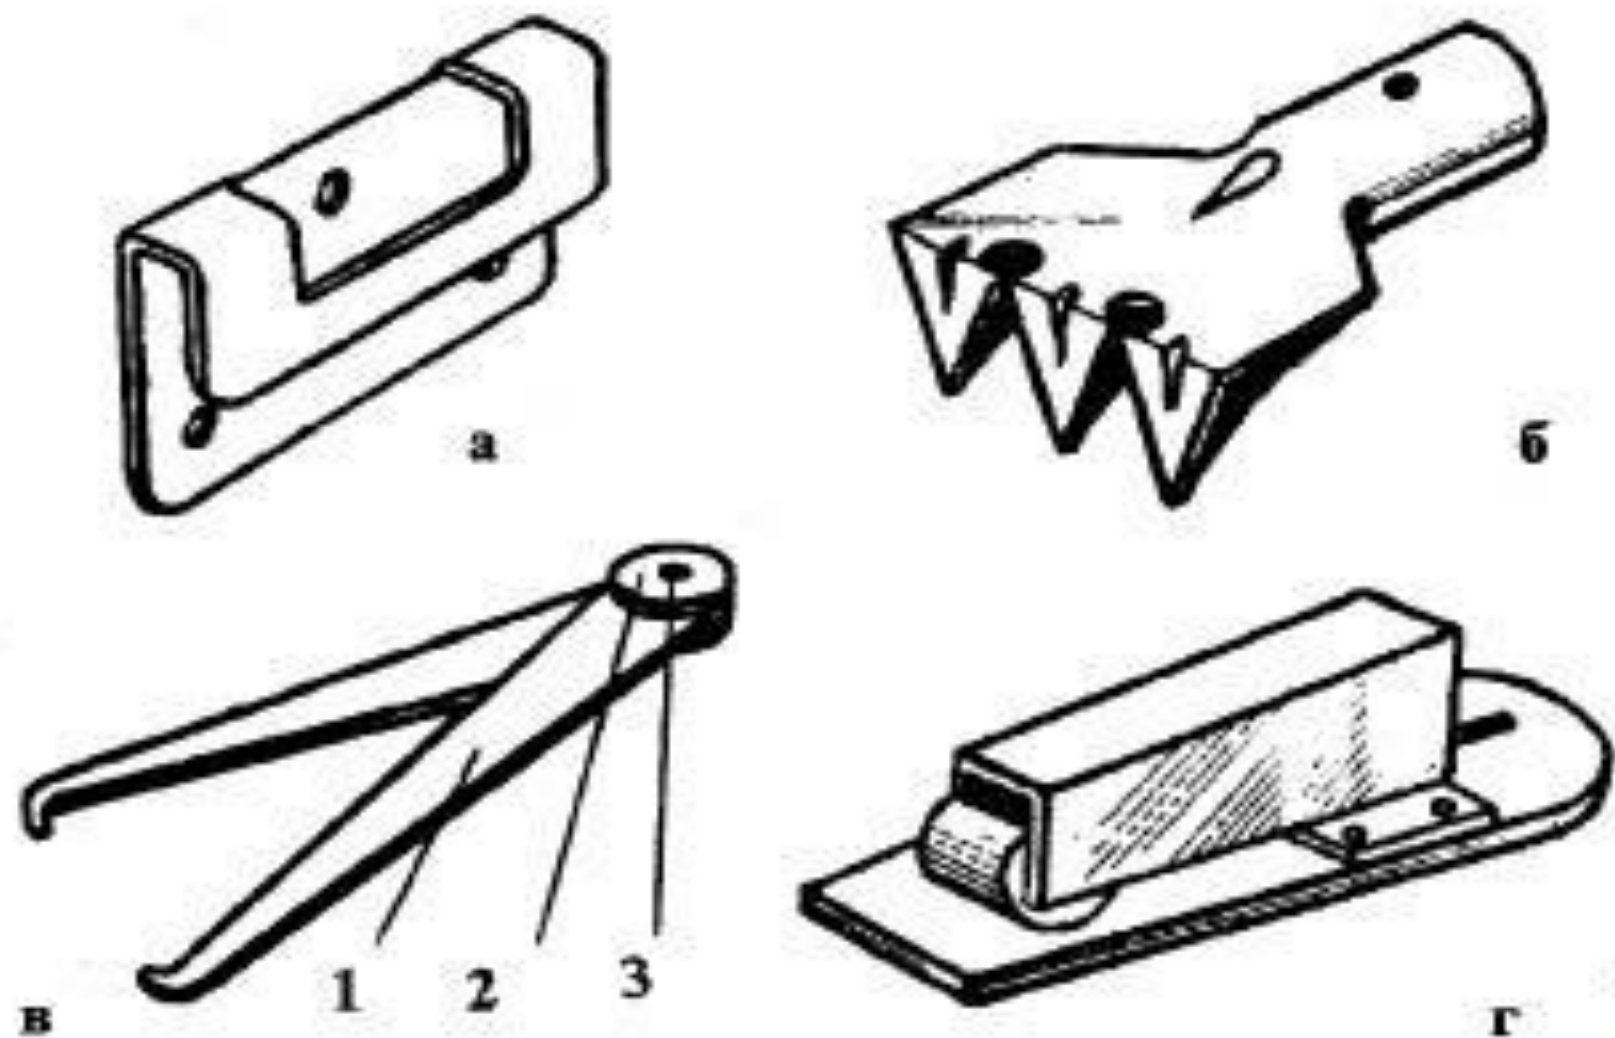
Изделия из сортового проката: а — ручка для дверки шкафчика, ящика; б — рыхлитель; в — нутромер: 1 — ножка; 2 — шайба; 3 — ось; г — зажим для таблиц
